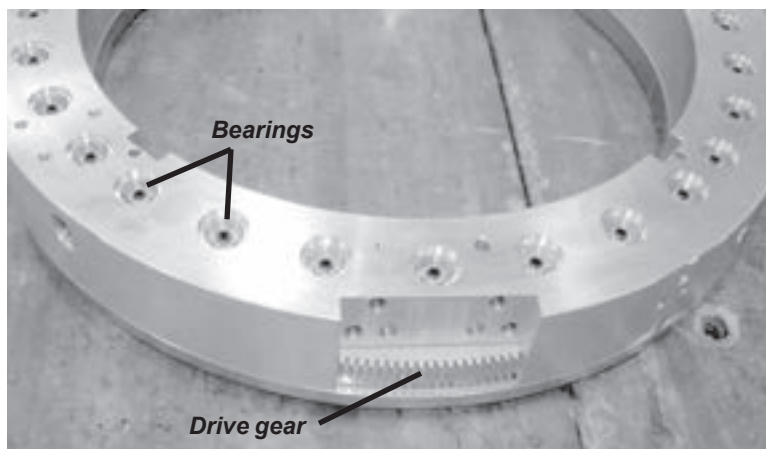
Los rodamientos y engranajes de accionamiento están encerrados en la cortadora LCSF. La caja del piñón cubre los engranajes de accionamiento cuando se instala.
